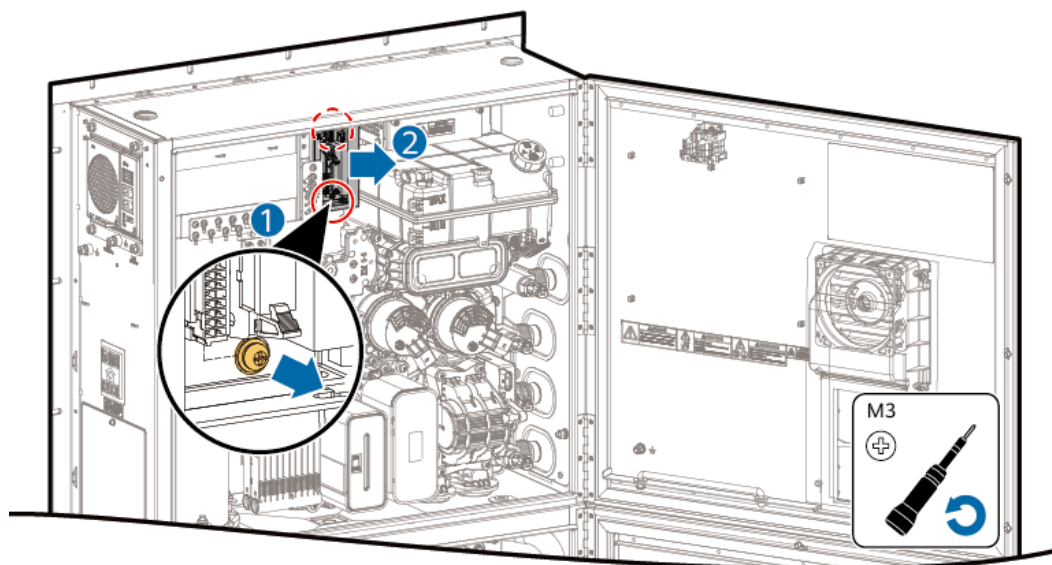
Entfernen der Abdeckung von der Hauptsteuerungs-Backplane
